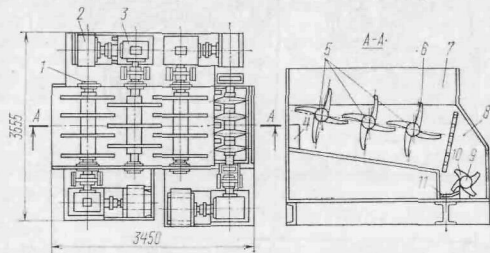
Валковая стружкодробилка конструкции УЗТМ
